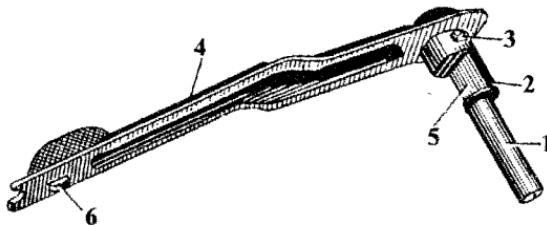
Предохранитель СВД-63: 1 — ось; 2 — утолщенная часть оси; 3 — выступ оси; 4 — щиток; 5 — вырез для хвоста шептала; 6 — выступ щитка.
